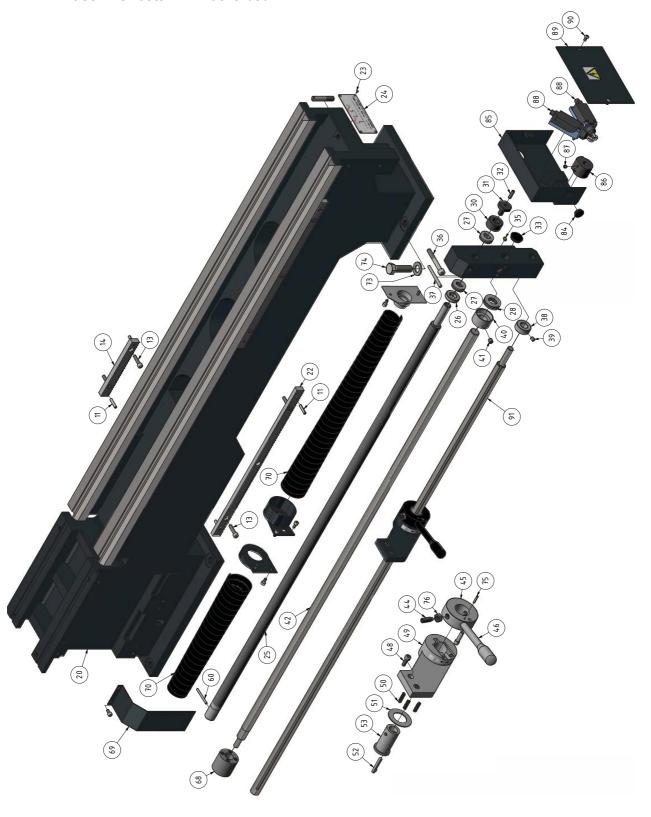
Maschinenbett 2-2 - Lathe bed 2-2
